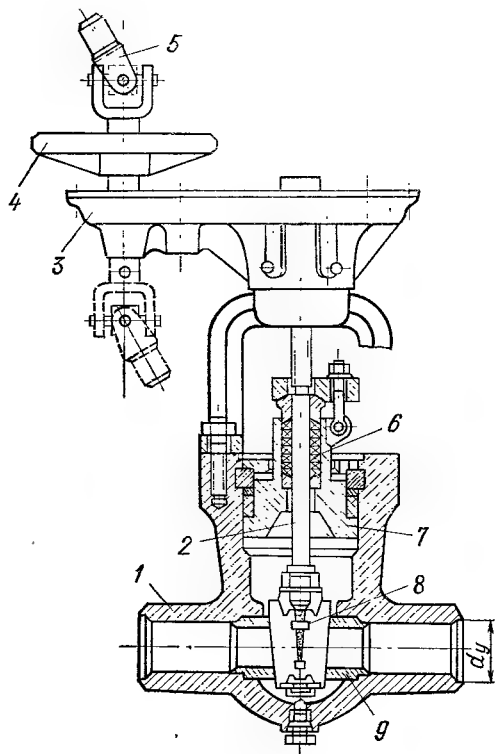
Задвижка $d_y=100 \div 300$ мм ЧЗЭМ с приводной головкой и цилиндрической зубчатой передачей на параметры воды до 38 МПа и 280°C и пара до $25,5$ МПа, 565°C (соединение корпуса с крышкой бесфланцевое).
